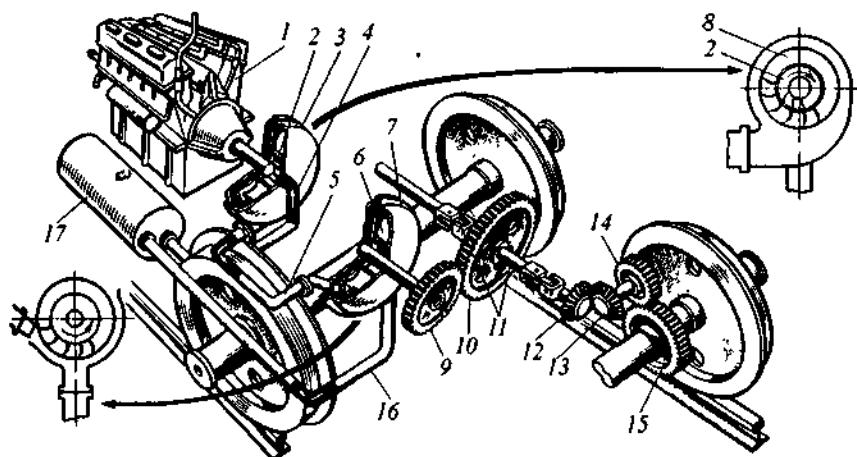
Схема гидродинамической передачи: 1 — дизель; 2 — рабочее колесо насоса; 3 — центробежный насос; 4, 5 — трубопроводы; 6 — колесо турбины; 7 — гидротурбина; 8 — направляющий аппарат насоса; 9, 10 — шестерни механической передачи; 11 — карданные валы; 12, 13, 14, 15 — шестерни осевого редуктора; 16 — сливная труба; 17 — резервуар для рабочей жидкости
